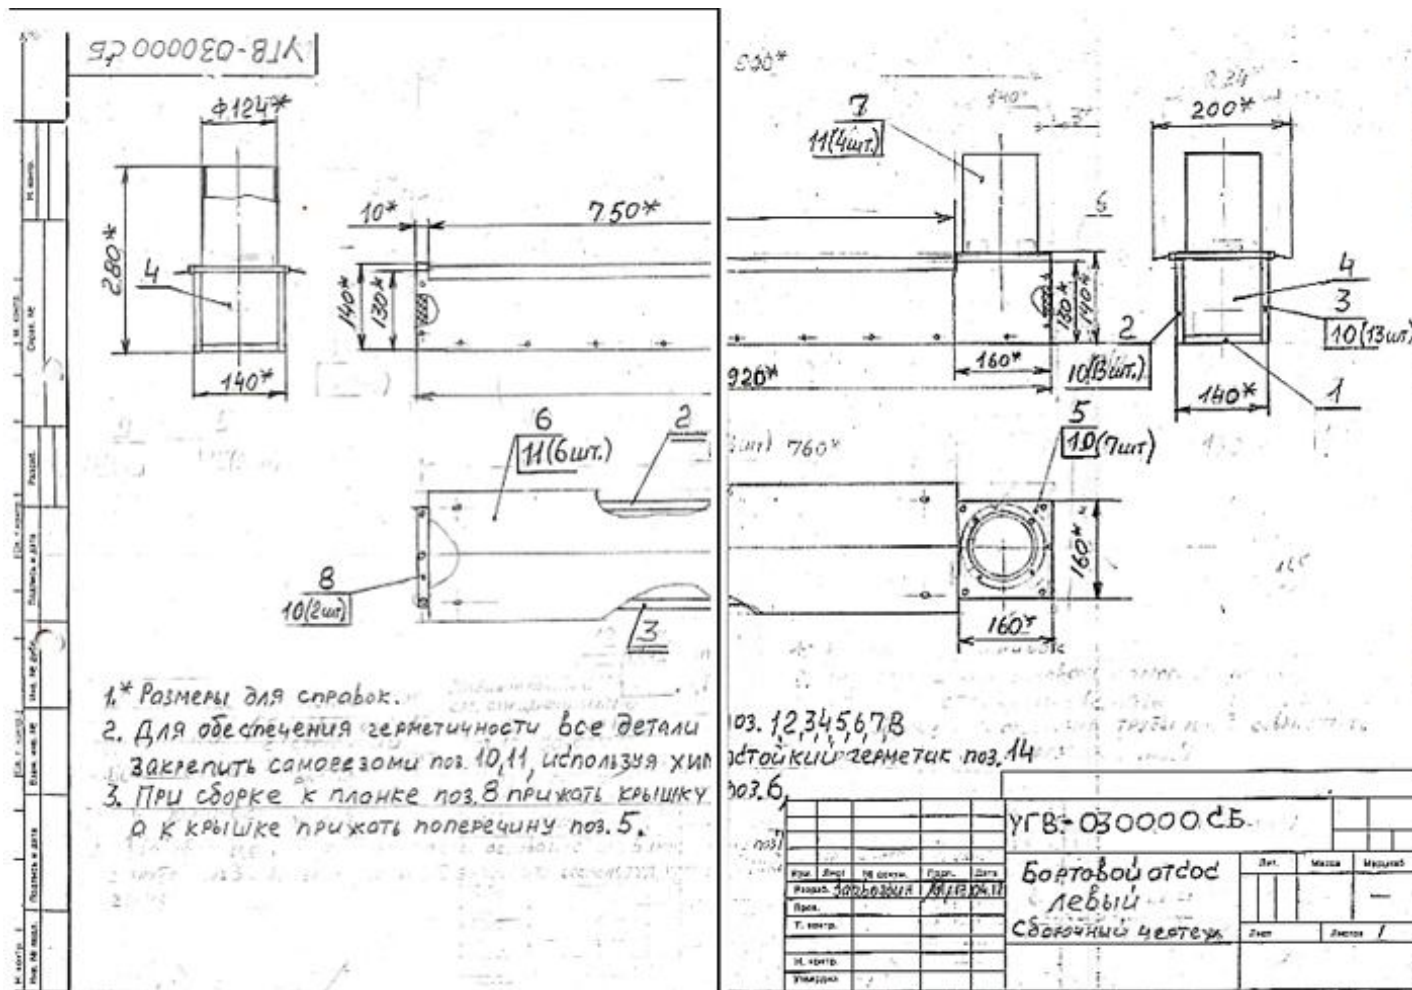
Сборочный чертеж на левый бортовой отсос
